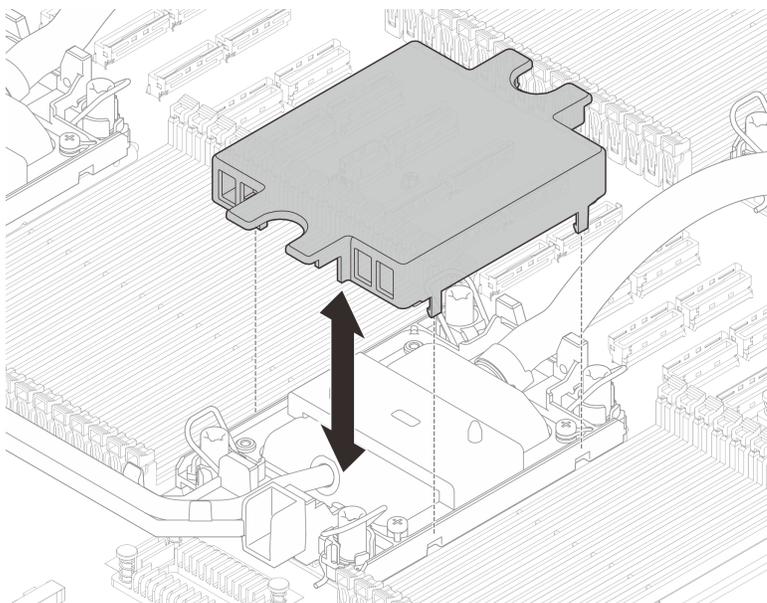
Entfernen der Kühlplattenabdeckungen
